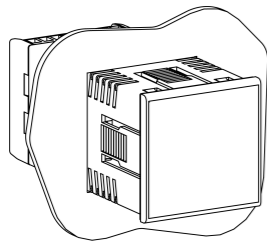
Монтаж прибора щитового крепления Щ5
